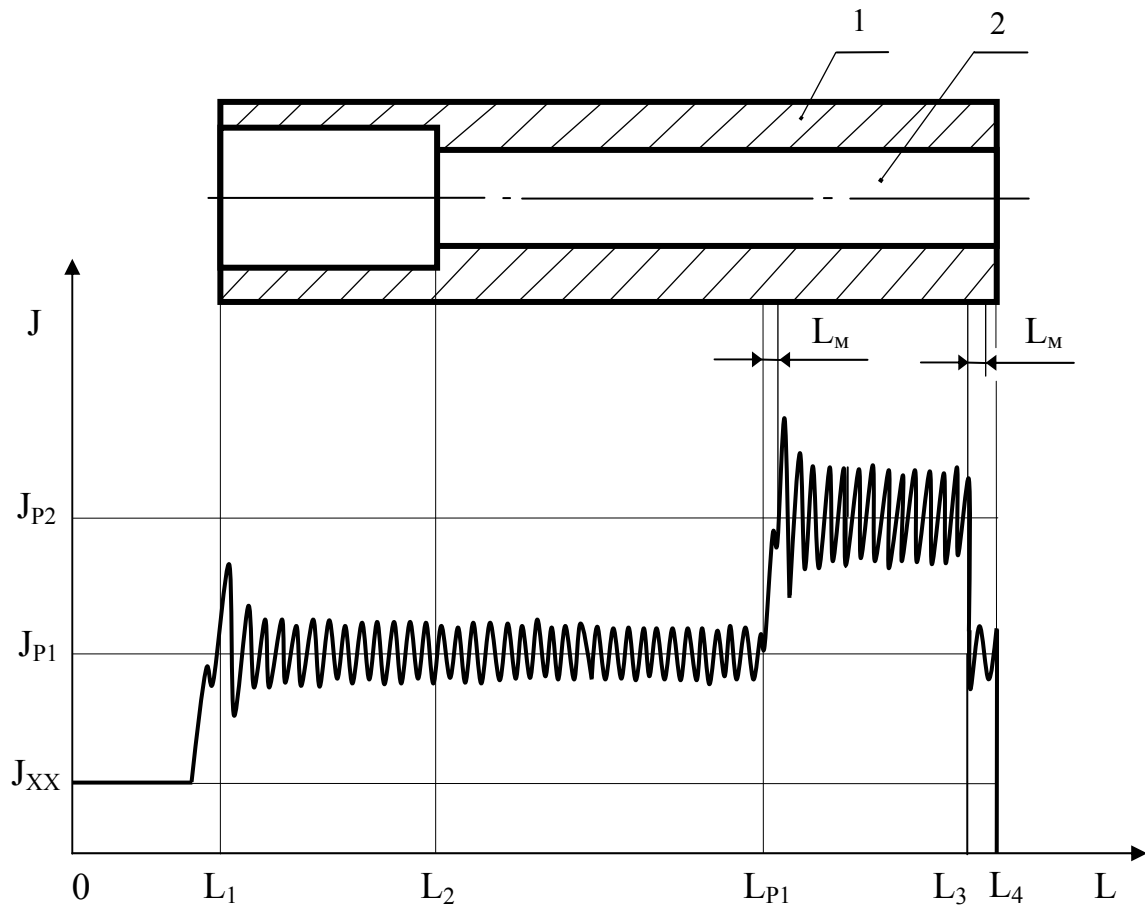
Заготовка со ступенчатым отверстием и график фактических значений тока  $J$  якоря привода главного движения в зависимости от относительного положения  $L$  заготовки и расточного инструмента: 1 – заготовка, 2 – ступенчатое отверстие.
